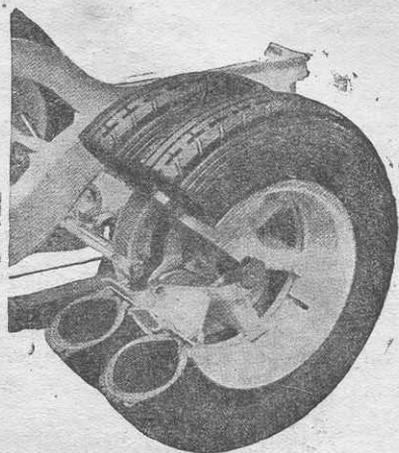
а. Разрез заднего колеса автомобиля «Мерседес-Бенц» с зубчатым приводом в ступице.
